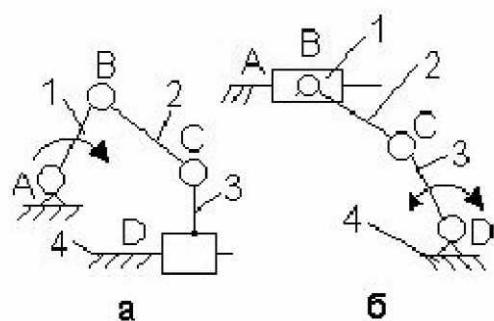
Схемы четырехзвенного рычажного механизма;
